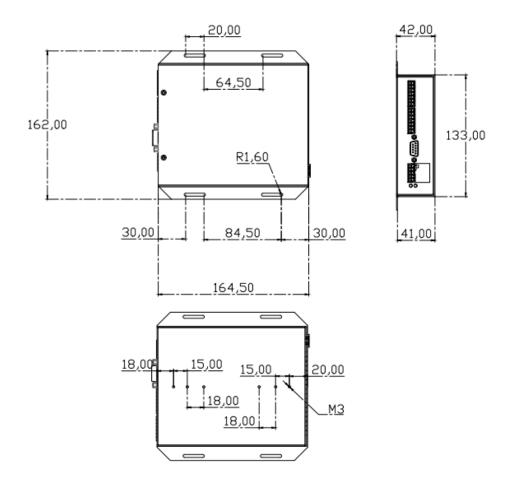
Размеры основного блока контроллеров ТНС F1627S/F1627D.
